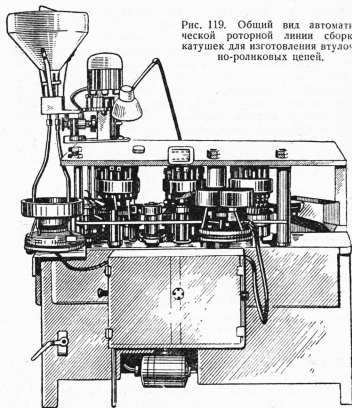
Общий вид автоматической роторной линии сборки катушек для изготовления втулочно-роликовых цепей.
